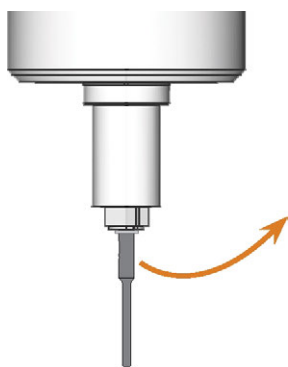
RIMOZIONE DELL'UTENSILE DALLA PINZA DI SERRAGGIO
